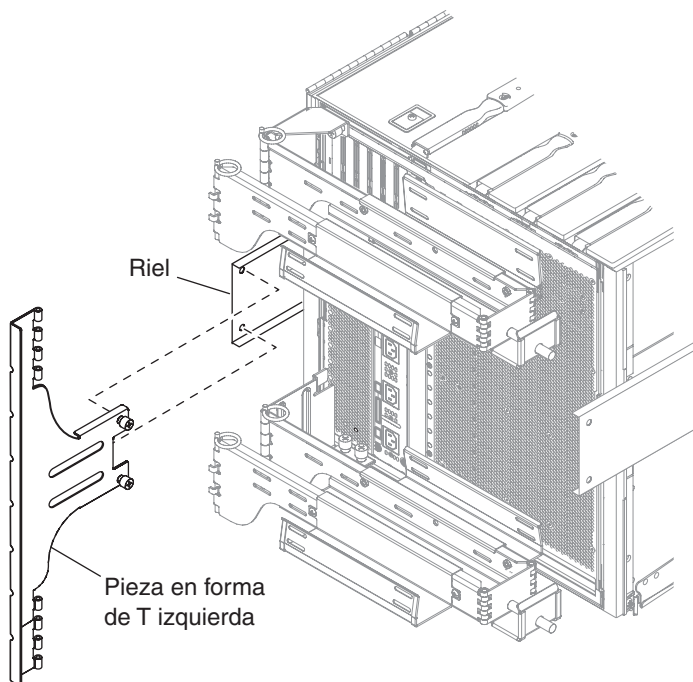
Montaje de la pieza en forma de T izquierda
